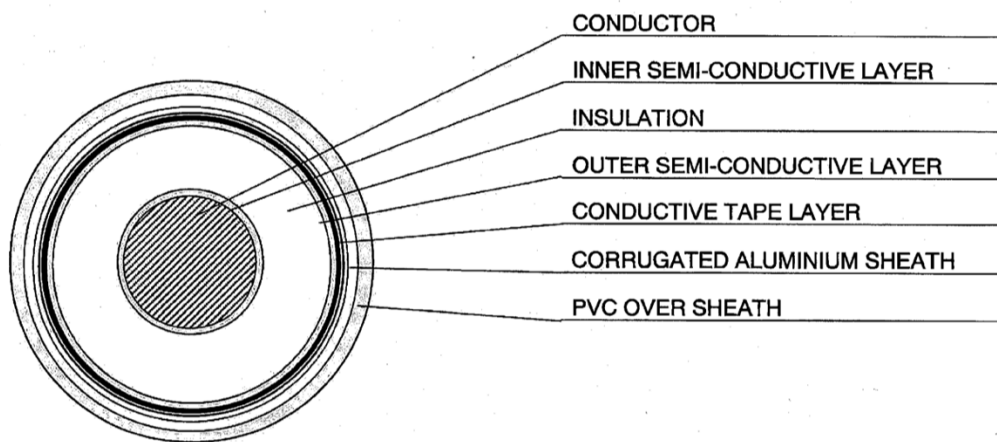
Construction d'un câble CAS 69kV avec gaine en aluminium ondulé
